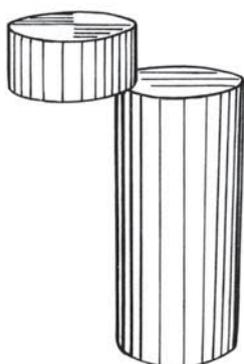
Форма торцов заготовки при закрытой отрезке с осевым сжатием
